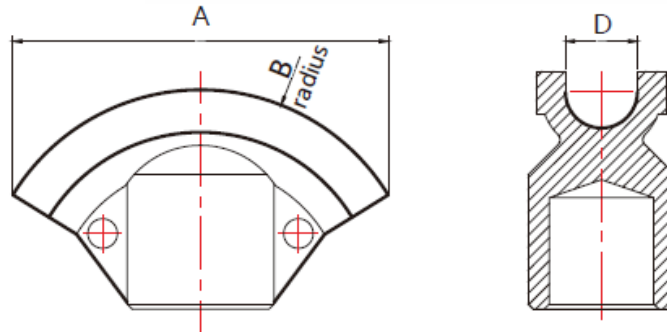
Конструкция ручного гидравлического трубогиба VOLL V-Bend
